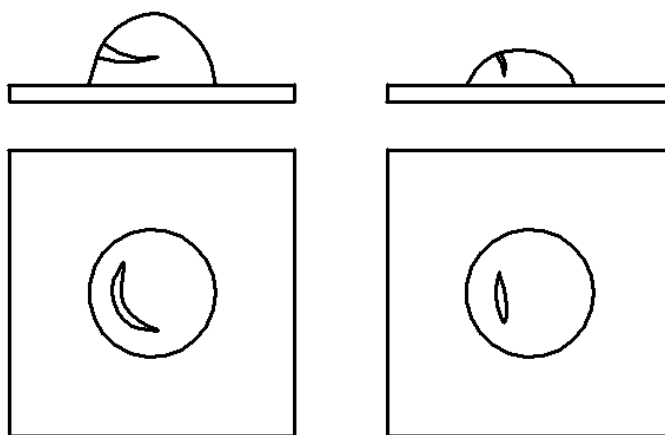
Schéma zkoušky hloubením dle Erichsena [6]
